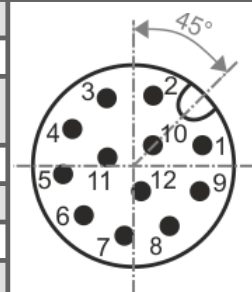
I/O-Steckverbinder, Sicht auf Kamera
